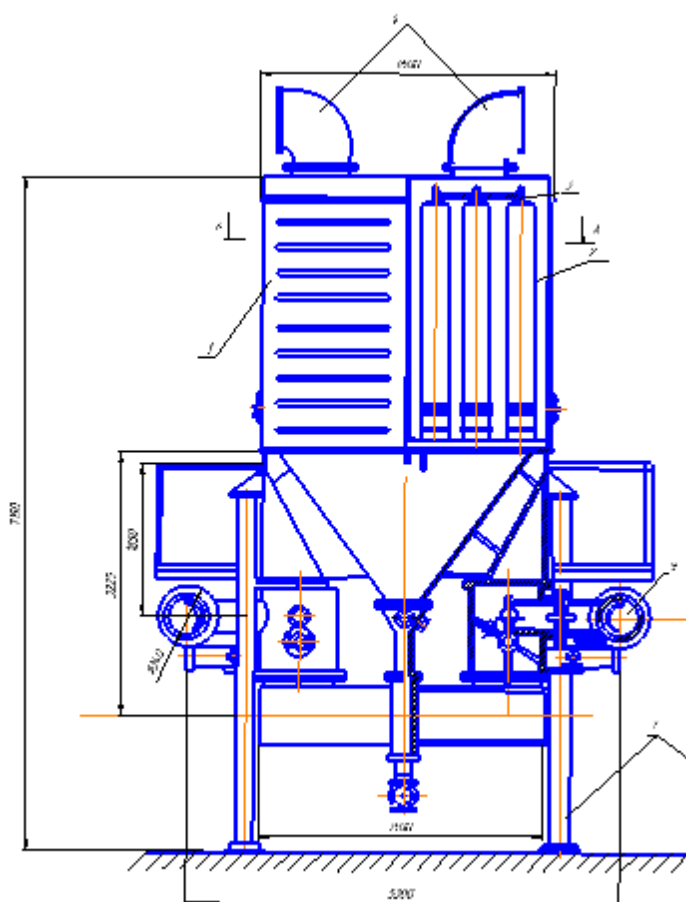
Схема типової конструкції конструкції рукавного фільтра
